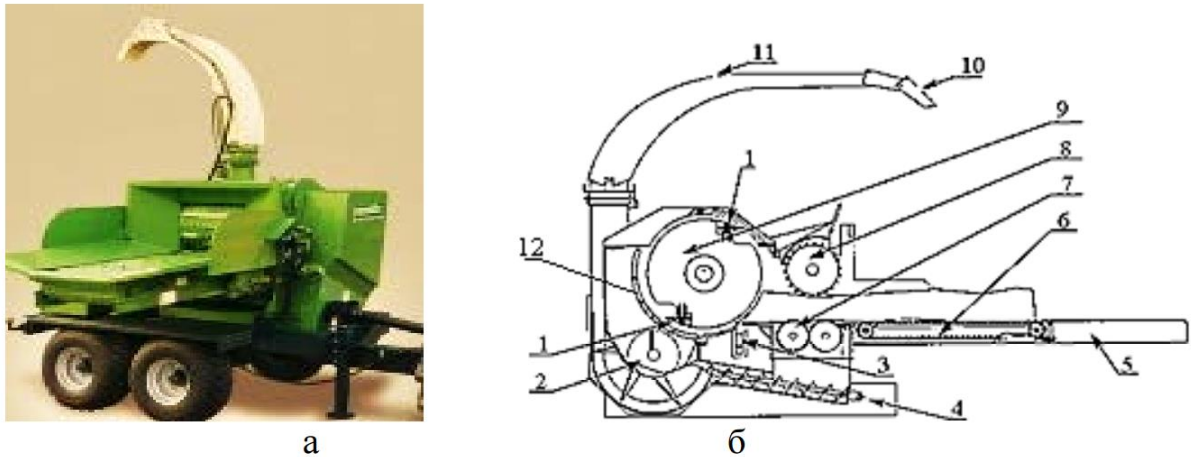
Подрібнювальна машина гілок з барабанним різальним пристроєм: а – загальний вигляд; б – конструкційна схема.
